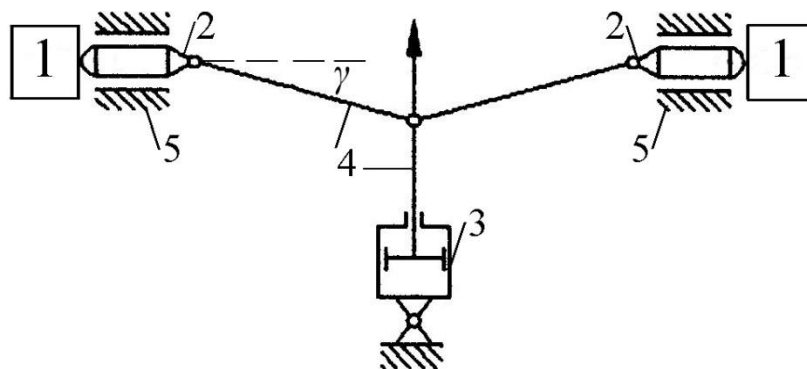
Схема нагружения в маложесткого кольца 1 плунжерами 2 в устройстве по патенту [12]. 3 – гидропривод, 4 – рычажно-шарнирный механизм, 5 – корпус, γ – угол наклона рычага
